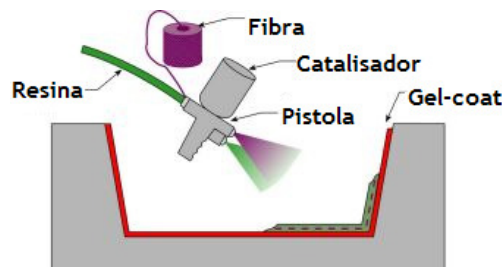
Esquema representativo do processo de Laminagem por Projecção. (11)
